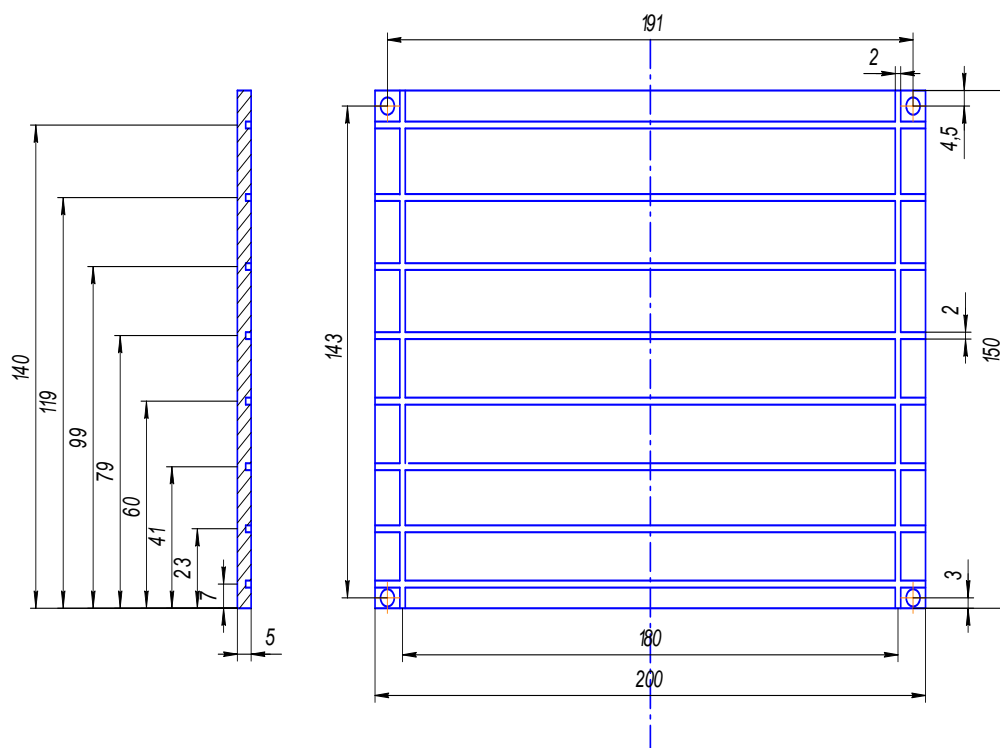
Пластина с канавками для нагревателя, выполненными с переменным шагом
